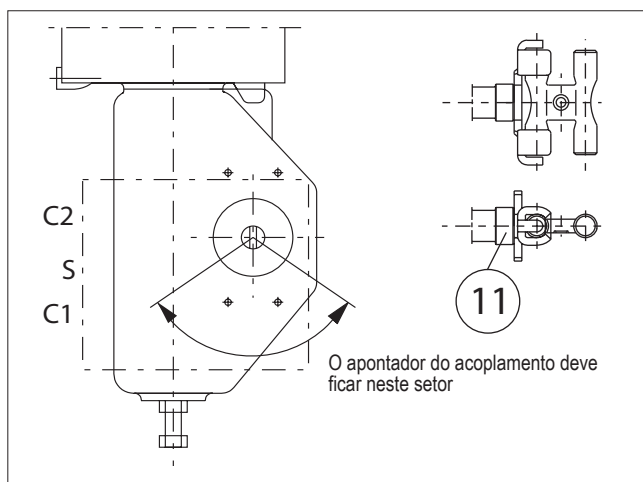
Montagem em atuador Neles com face de montagem VDI/VE
